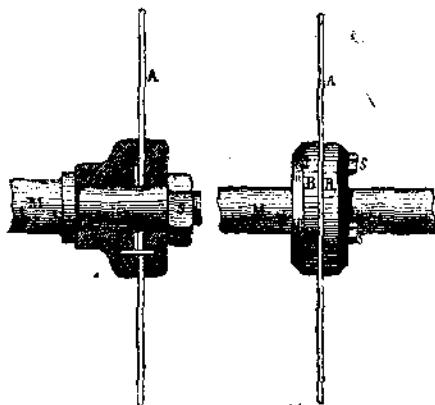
Простейший способ закрепления круглой пилы на валу.
